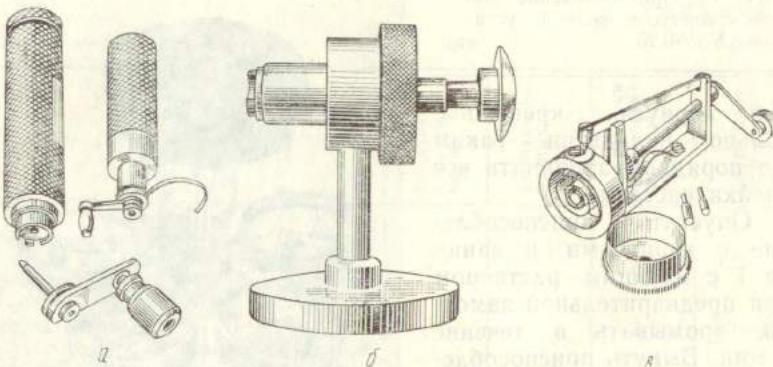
Приспособления для навивки и вставки пружины в барабан:
